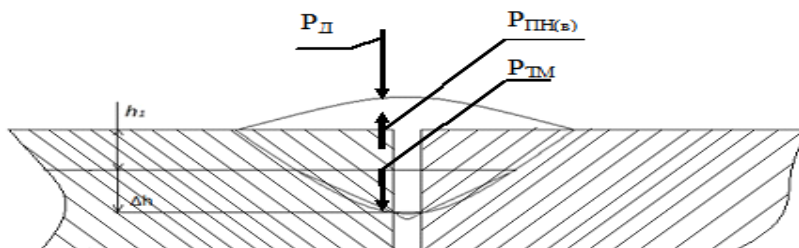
Схема сварки пластин и схема действия сил на расплавленный металл
